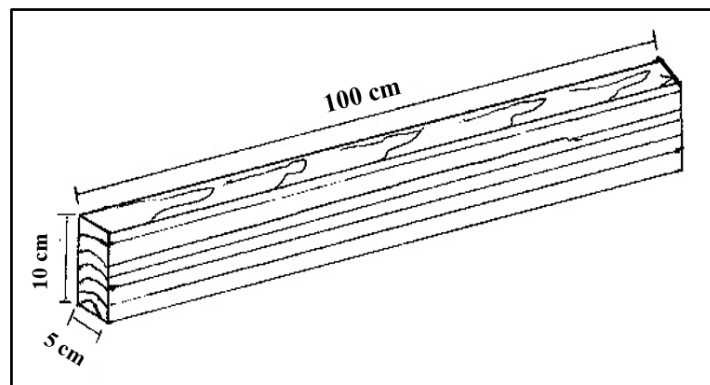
Dimensión de Probeta Destinada a Ensayos de Moldurado.
